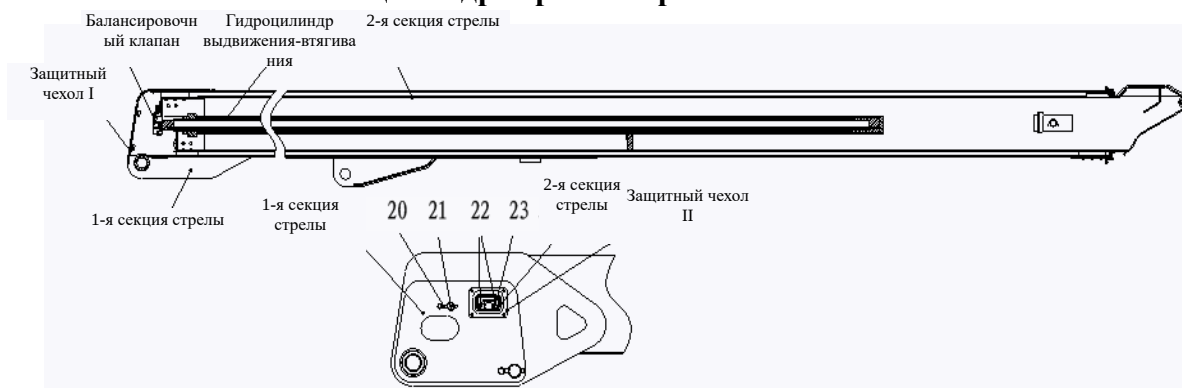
Схема разборки телескопического цилиндра верхней стрелы
